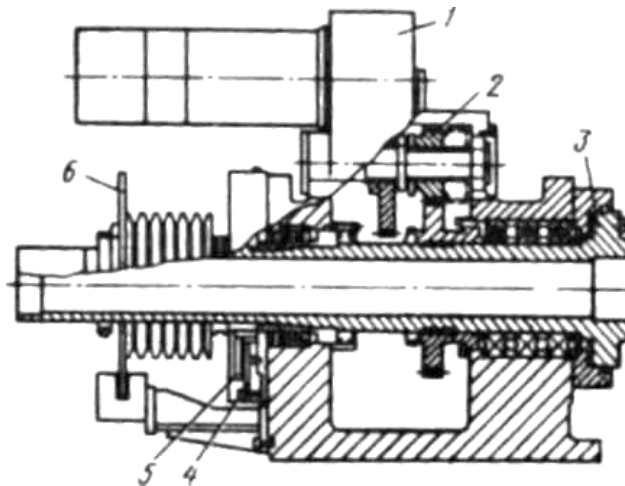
Управляемый шпиндель токарно-фрезерного многоцелевого станка
